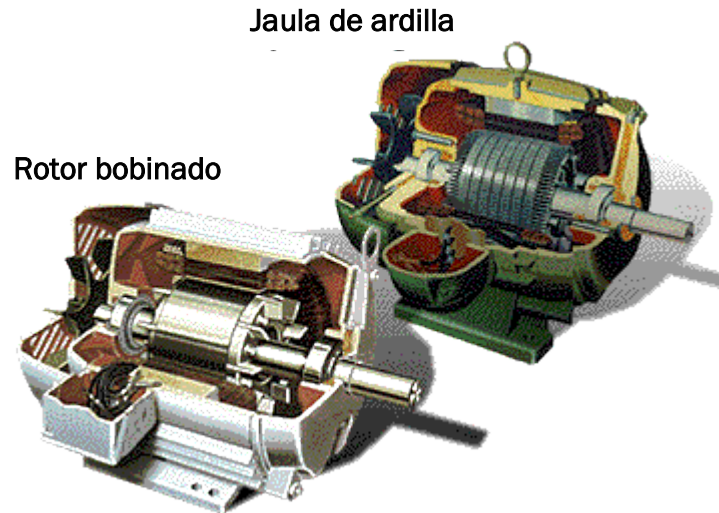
Sección motor de rotor bobinado y motor de jaula de ardilla.
